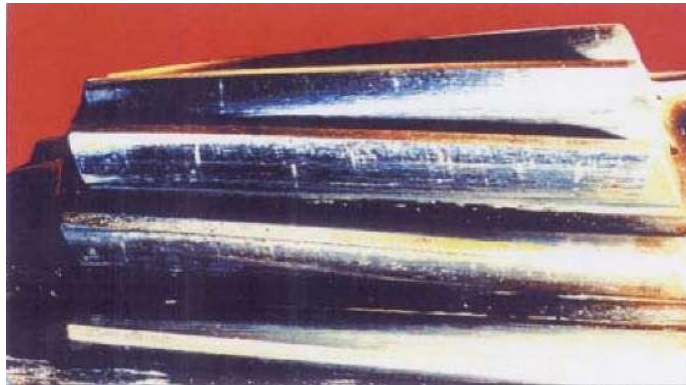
Загальний вид зубів зі слідами адгезійного зношування
